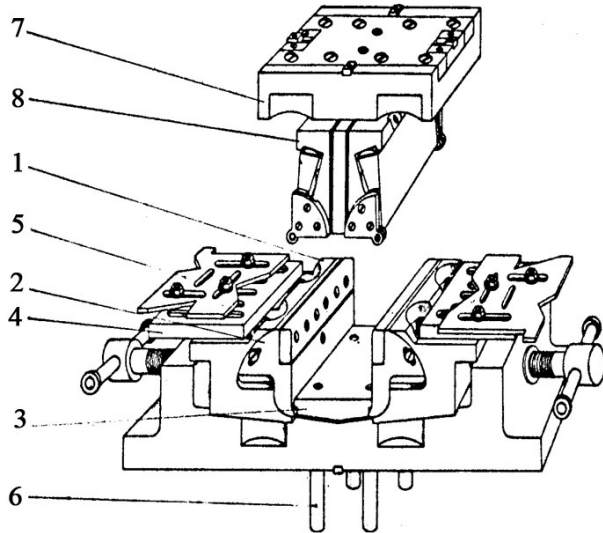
Сменный переналаживаемый пакет для двухугловой гибки деталей с заданными точностными параметрами расположения и формы поверхностей:
